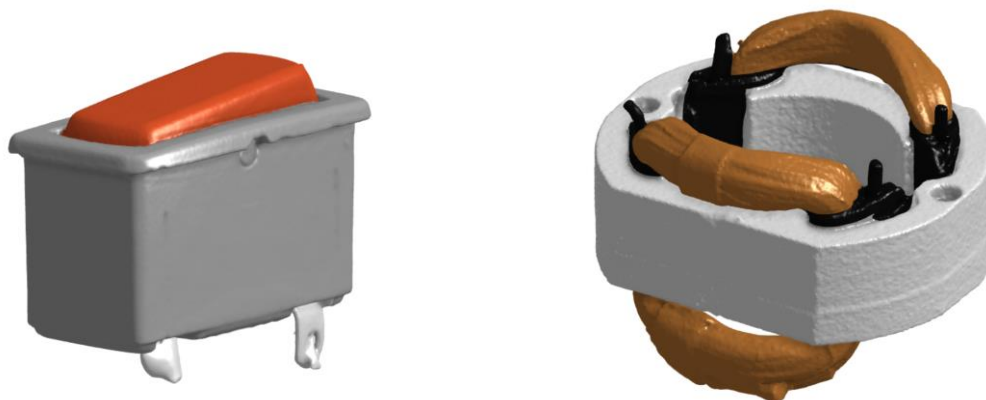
Jednobojna CAD modelirana (lijevo) i 3D skenirana komponenta (desno)
